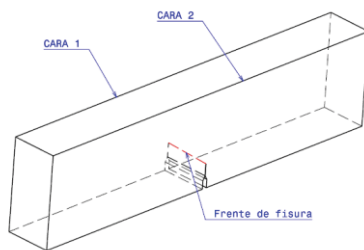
Esquema de la pieza tras el proceso de prefisuración.
